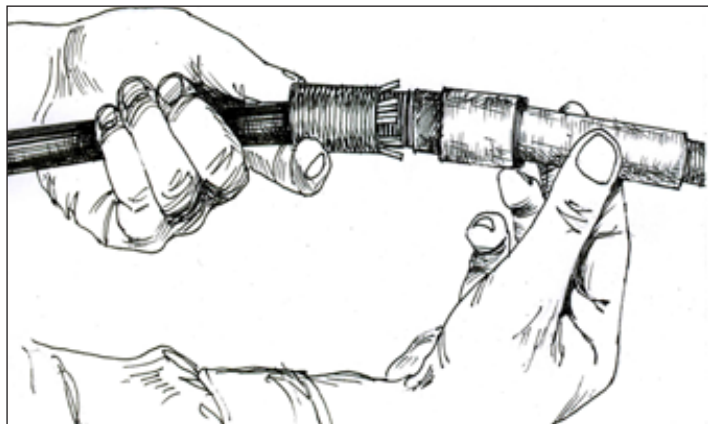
Установка внутренней гайки поверх проволоки
